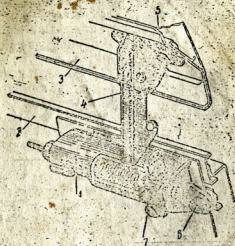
Замок багажника: 1 — корпус замка; 2 — панель кузова; 3 — крышка багажника; 4 — защелка; 5 — болты крепления защелки; 6 — латка крепления корпуса; 7 — стержень
